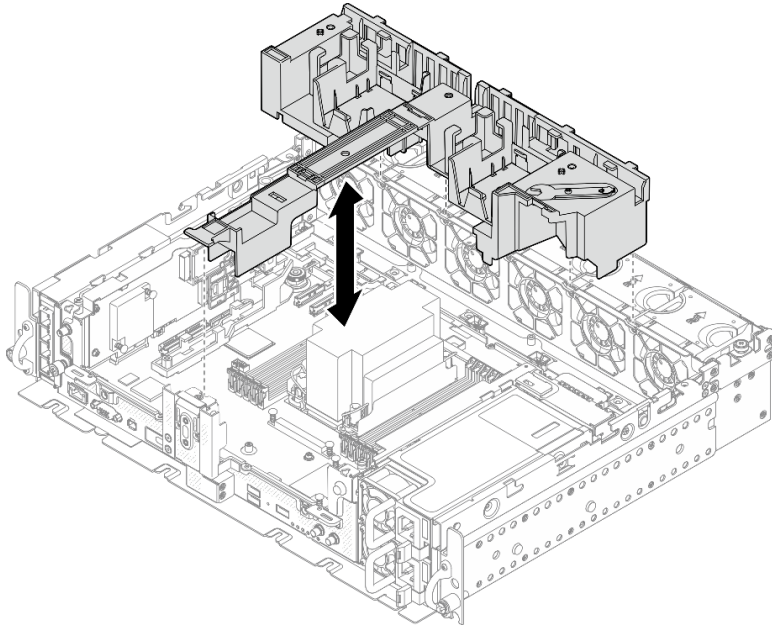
Entfernen der 360-mm-Luftführung (mit Adaptern mit voller Länge)
